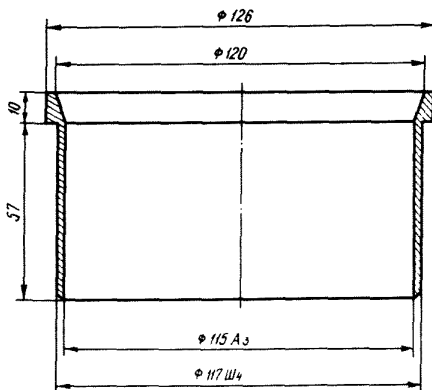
Приспособление для установки подвижного контакта камер в корпус
